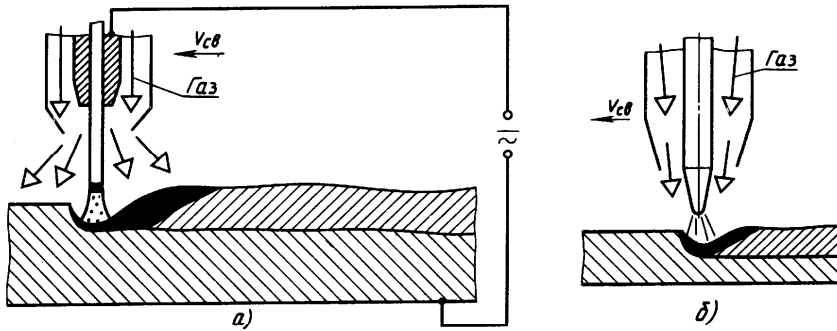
Схемы сварки в защитном газе плавящимся (а) и неплавящимся (б) электродами
